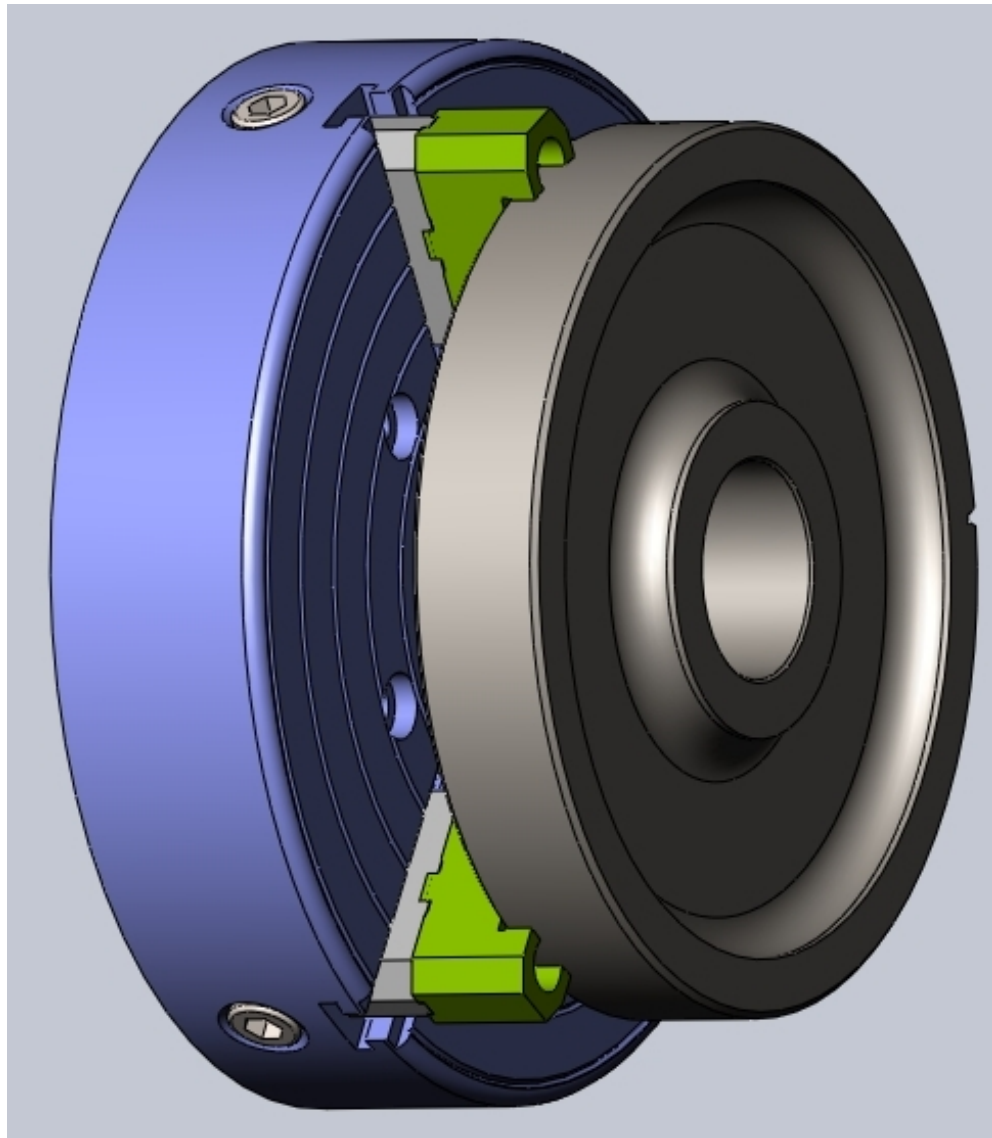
Пристрій для обробки поверхонь 1, 2, 3, 12
